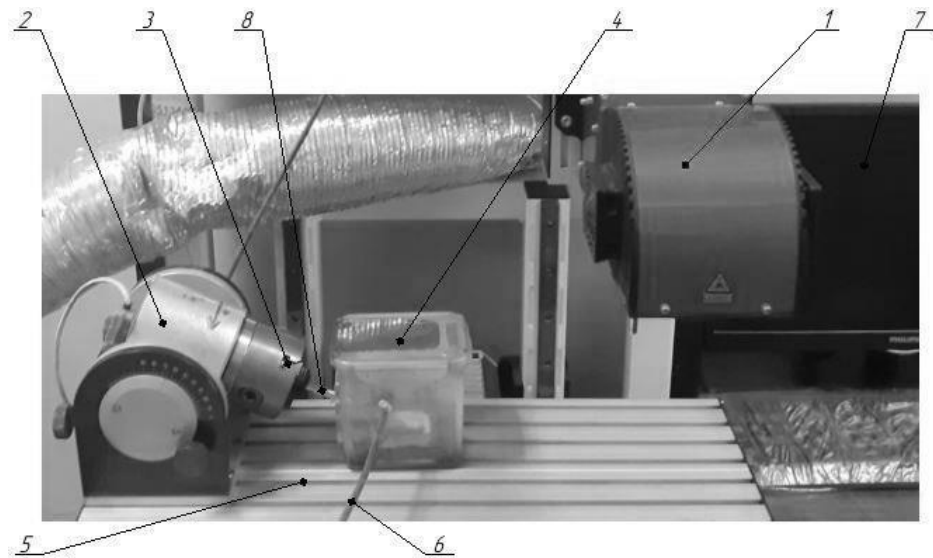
Установка для наплавлення зміцнювального покриття на поверхню робочої фаски клапана: 1 – лазерна установка; 2 – привід клапана; 3 – трикулачковий патрон; 4 – камера для наплавлення; 5 – стіл установки; 6 – трубка для підведення аргону; 7 – персональний комп'ютер для управління установкою; 8 – оброблюваний клапан
